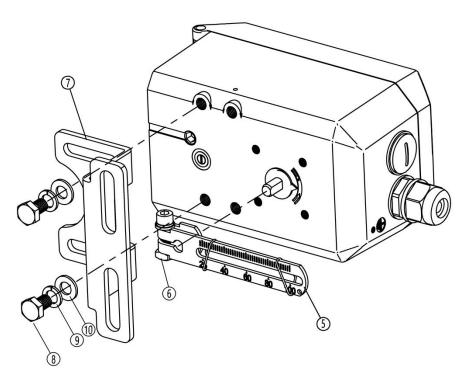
Рычаг обратной связи В и установка кронштейна крепления (обычного типа)
